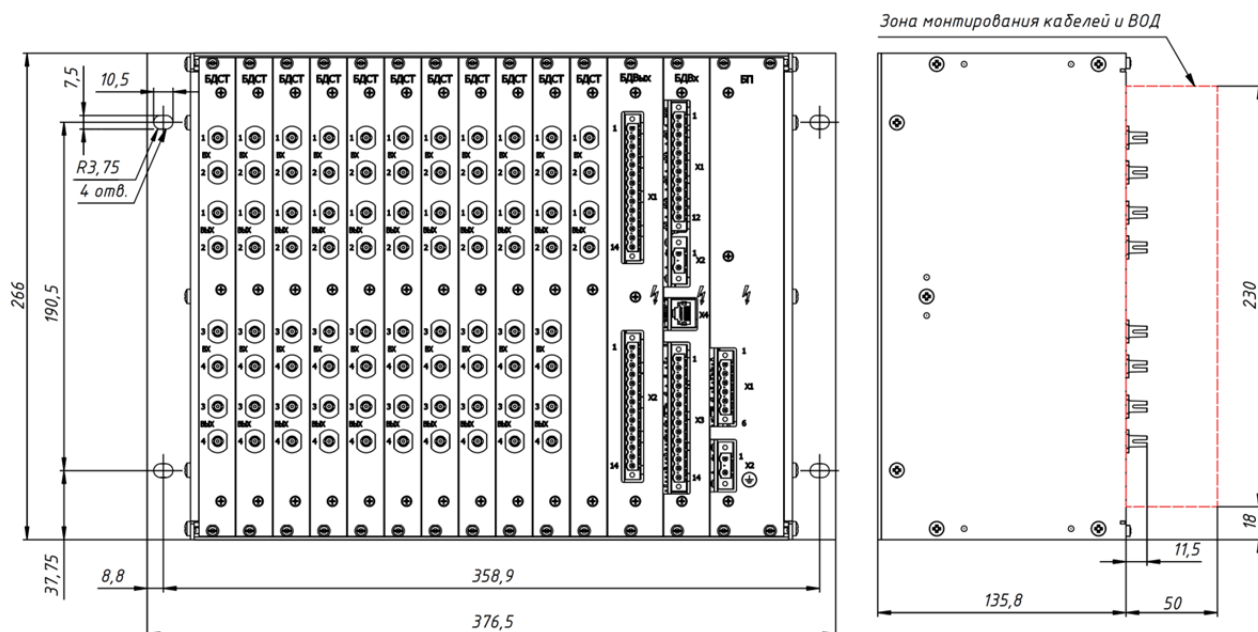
Внешний вид и габаритные размеры БПМ (исп.01).
